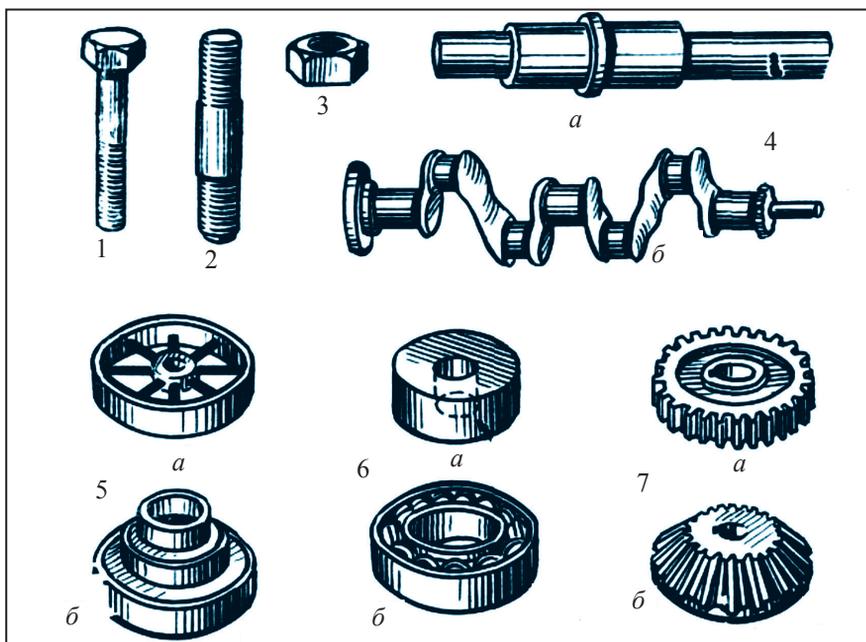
Образцы деталей машин: 1 – болт; 2 – шпилька; 3 – гайка; 4 – валы: *а* – прямые; *б* – коленчатые; 5 – шкивы: *а* – одноступенчатые, *б* – трёхступенчатые; 6 – подшипники: *а* – скольжения, *б* – качения; 7 – зубчатые колёса: *а* – цилиндрические; *б* – конусовидные.
